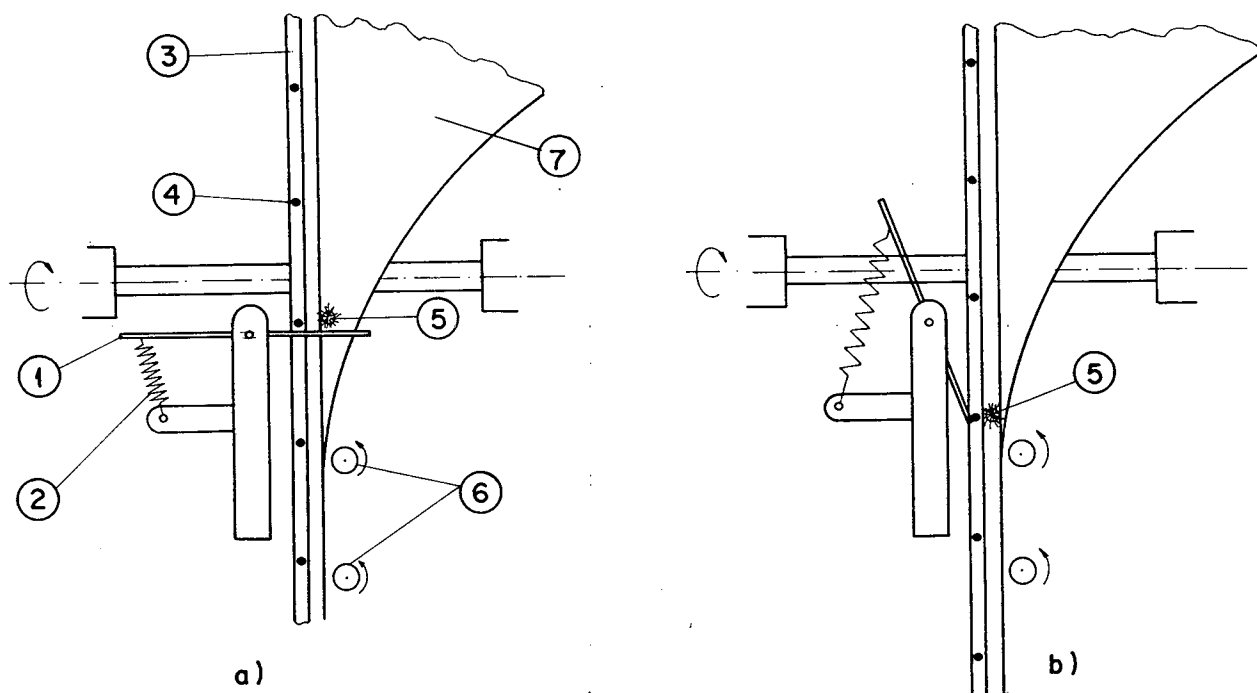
Vista frontal esquemática de dois instantes do dispositivo de placa móvel.
